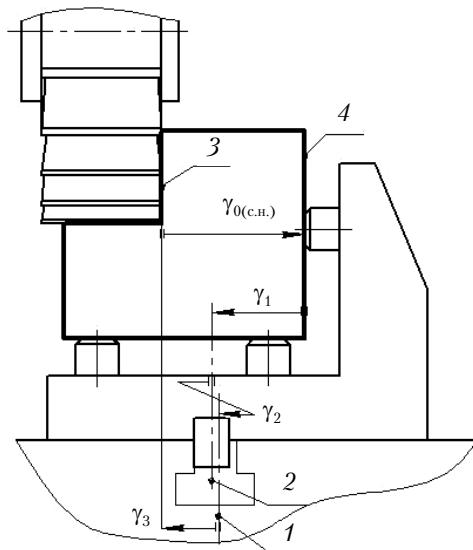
Схема формирования погрешности статической настройки при фрезеровании уступа на детали:
